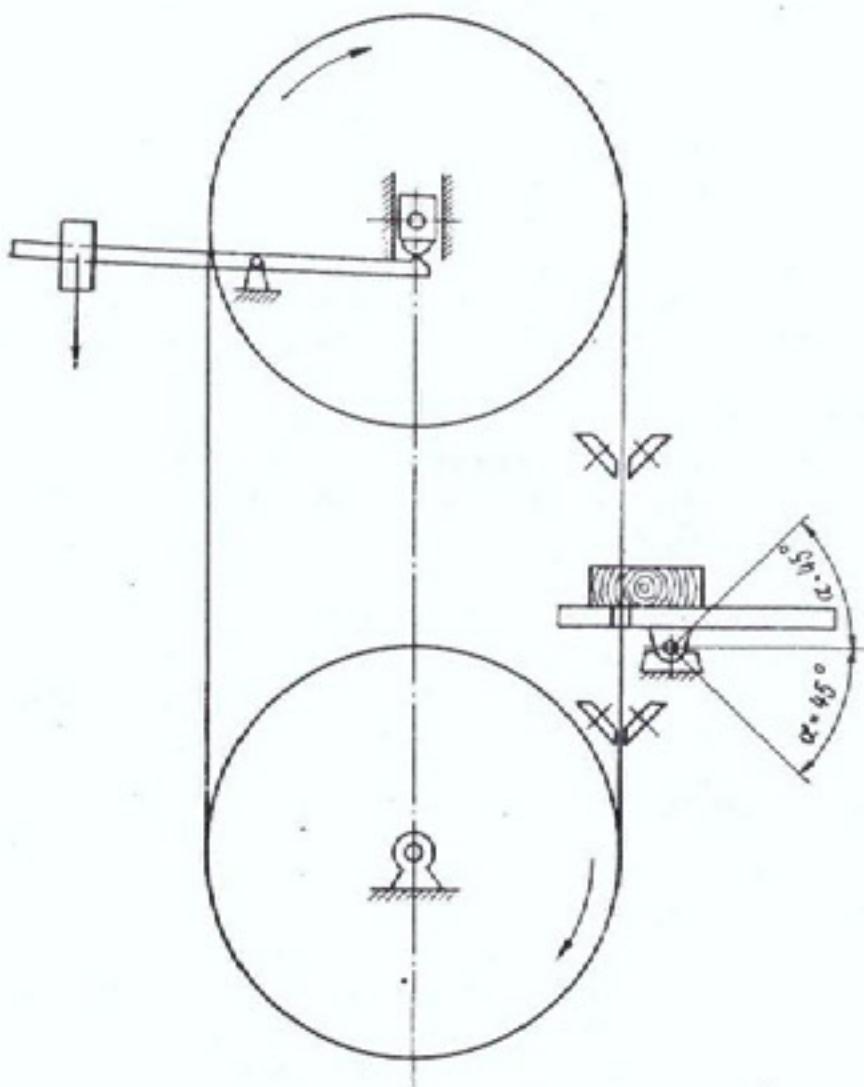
Кинематическая схема ленточнопильного станка столярного типа.
